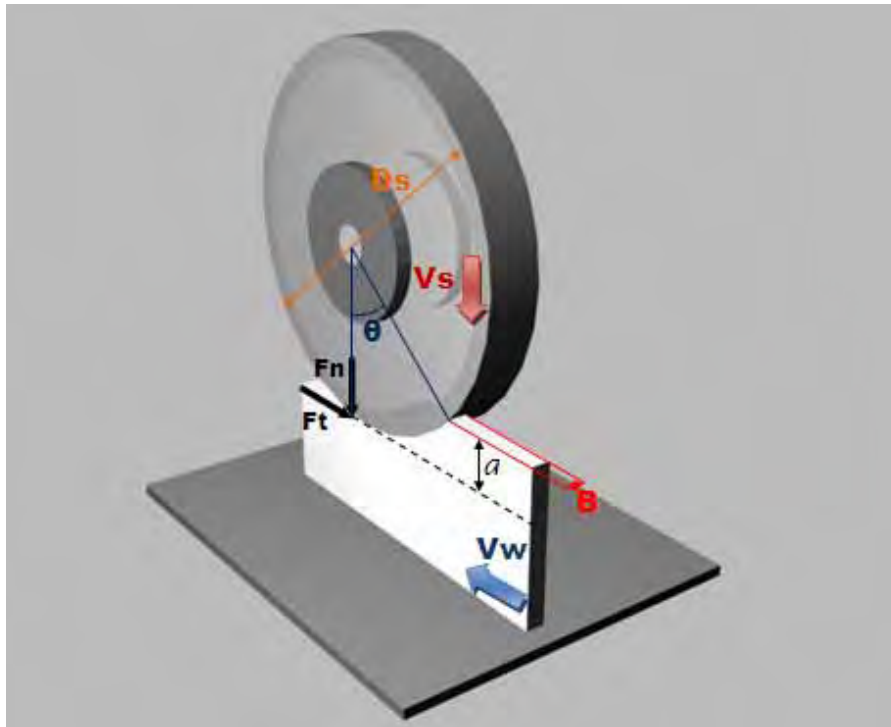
Esquema da retificação plana (adaptado de King & Hahn, 1986)
